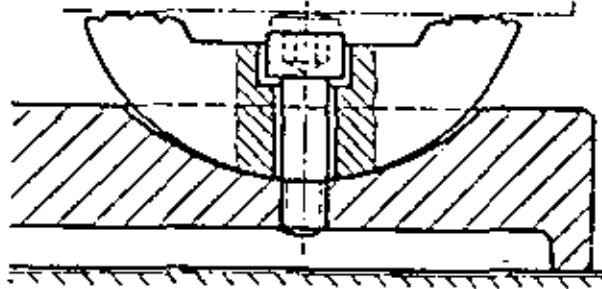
Palanca oscilante de apoyo con tornillo sujetador
